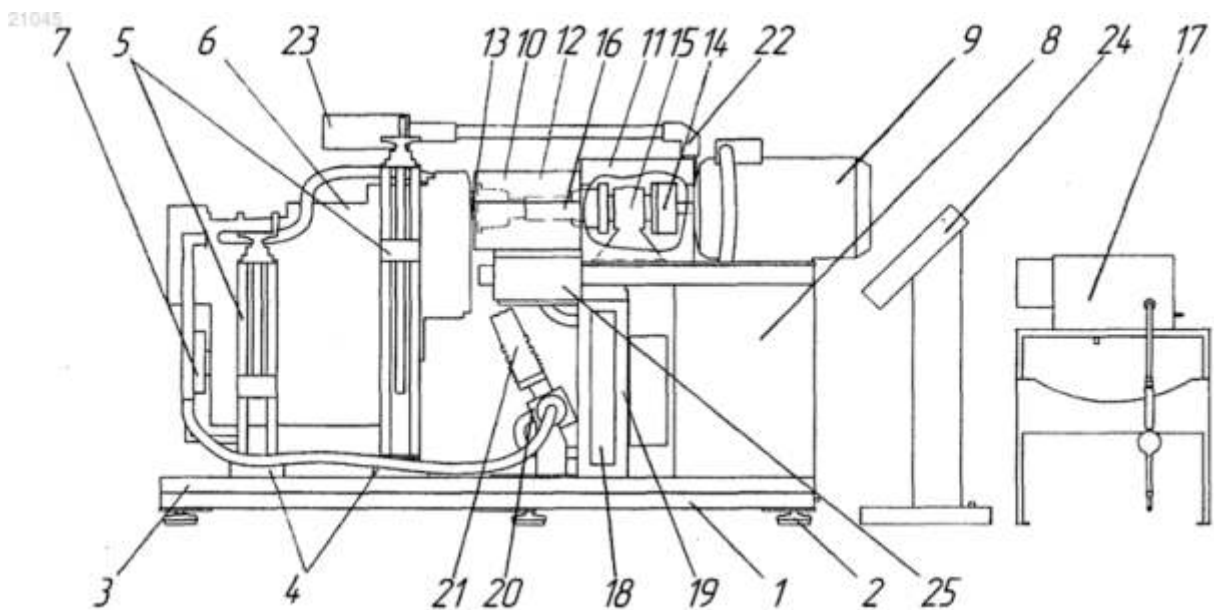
Стенд для обкатки и испытания коробки передач.
